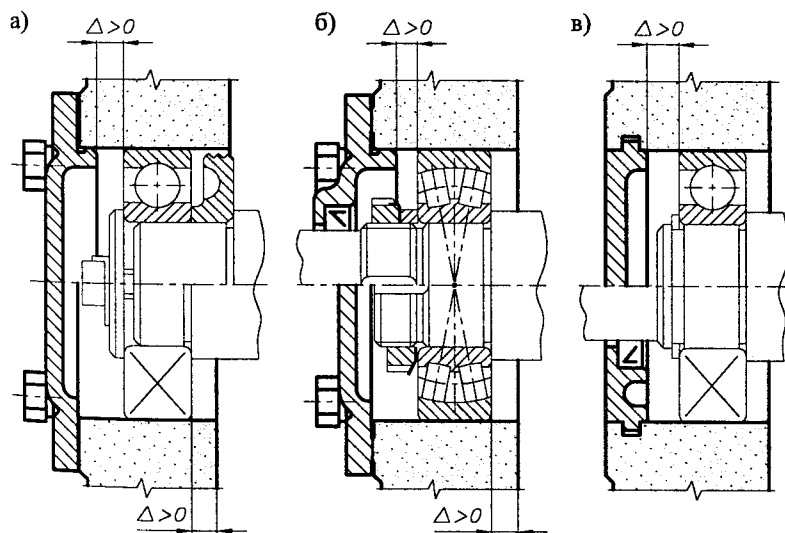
Установка наружного кольца неразъемного подшипника в корпусе плавающей (самоустанавливающейся) опоры
